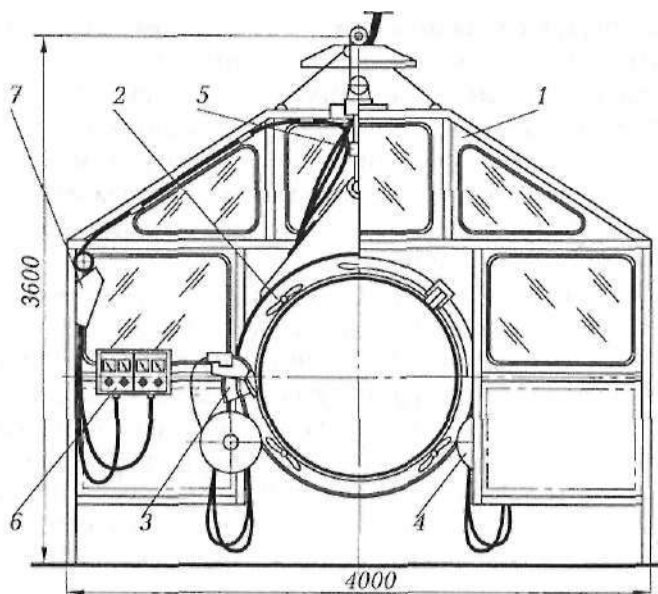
Сварочный аппарат А-1568:
